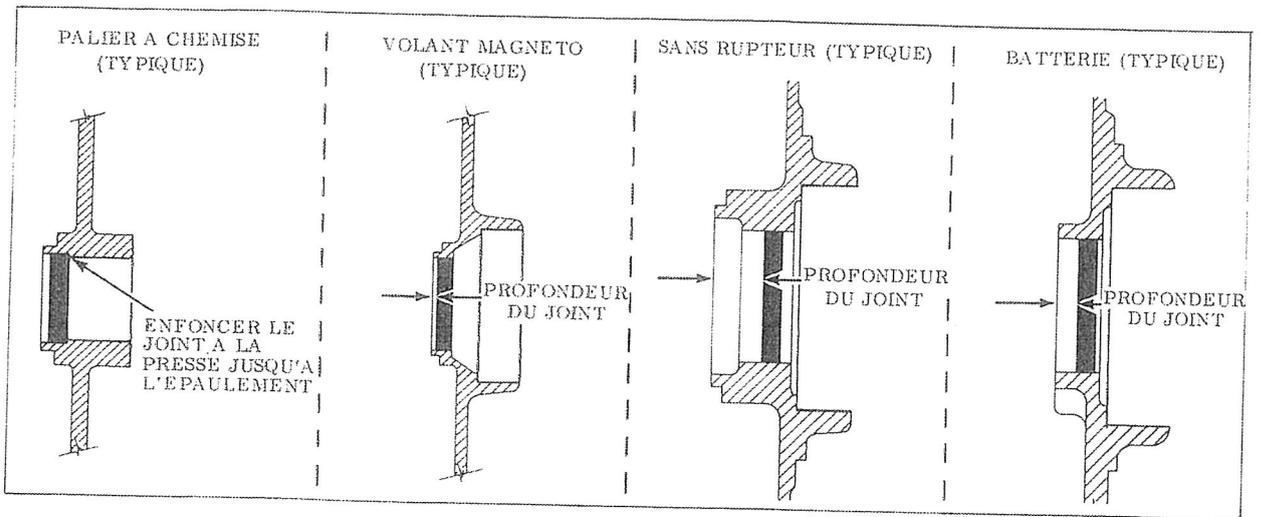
INSTALLATION DES JOINTS D'ETANCHEITE ARRIERE
